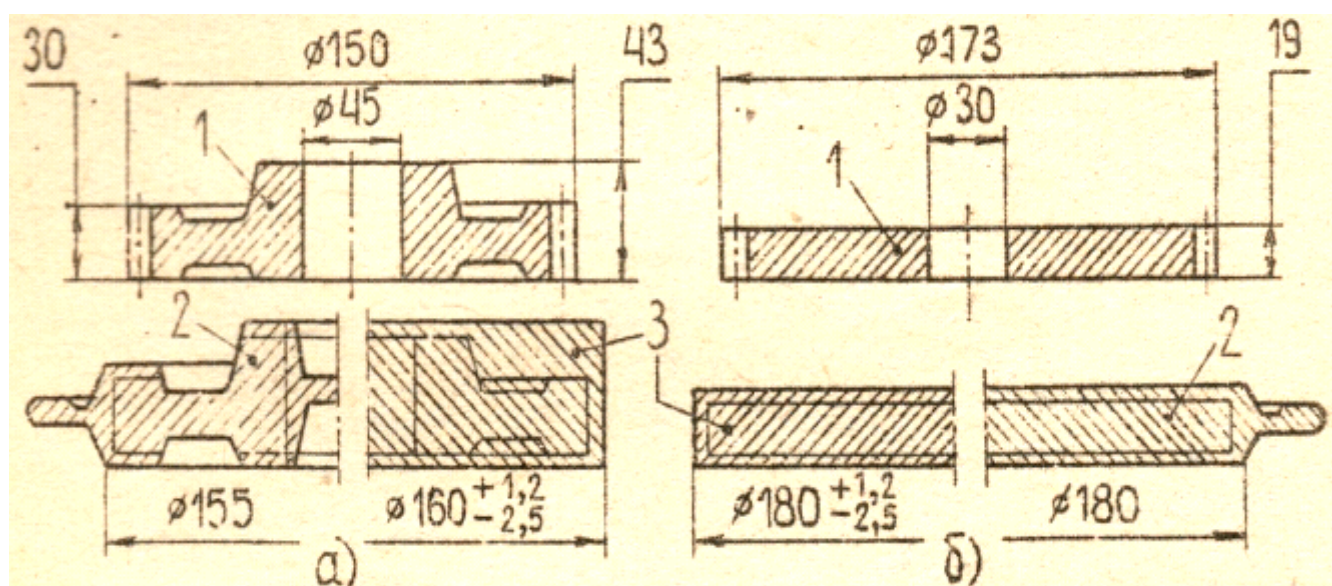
К выбору заготовки для зубчатого колеса сложной (а) и простой (б) конфигурации: 1 — деталь; 2 — штампованная заготовка; 3 — прокат
